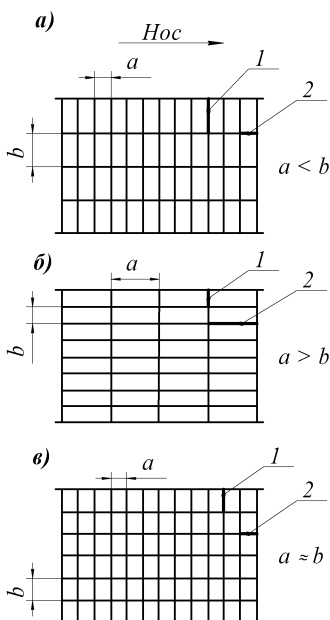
Схема расположения балок главного направления при различных системах набора корпуса: a – поперечной, b – продольной, $в$ – клетчатой; 1 – балки главного направления, 2 – перекрестные связи
